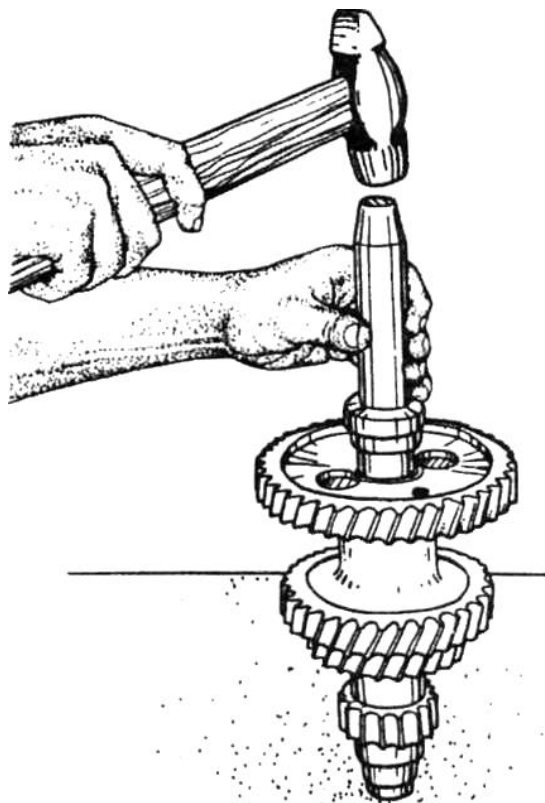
Напресування внутрішнього кільця роликового підшипника проміжного валу.
